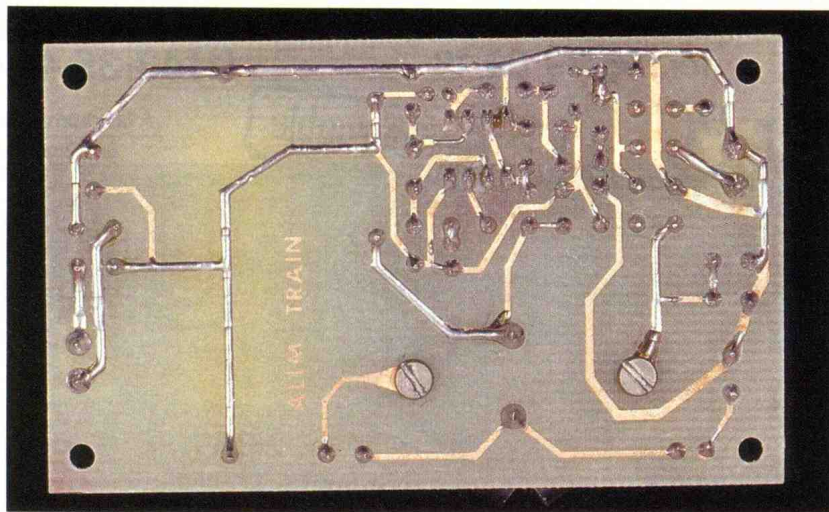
Vue d'avion sur le circuit imprimé côté soudures.
